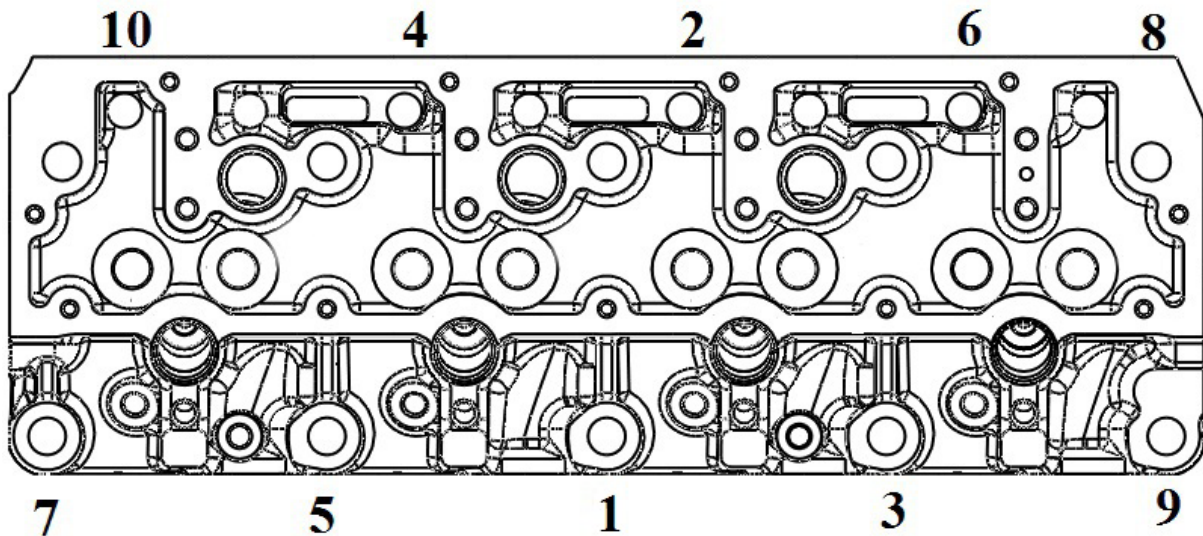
Схема последовательности затяжки болтов крепления головки цилиндров.
